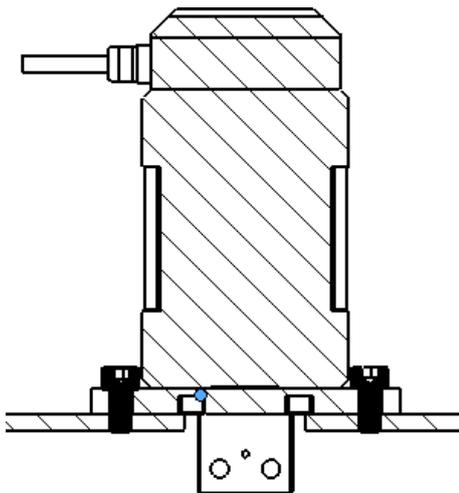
Beispiel für Montage mittels Montageflansch B (Schnittansicht mit hervorgehobenen Schrauben)
